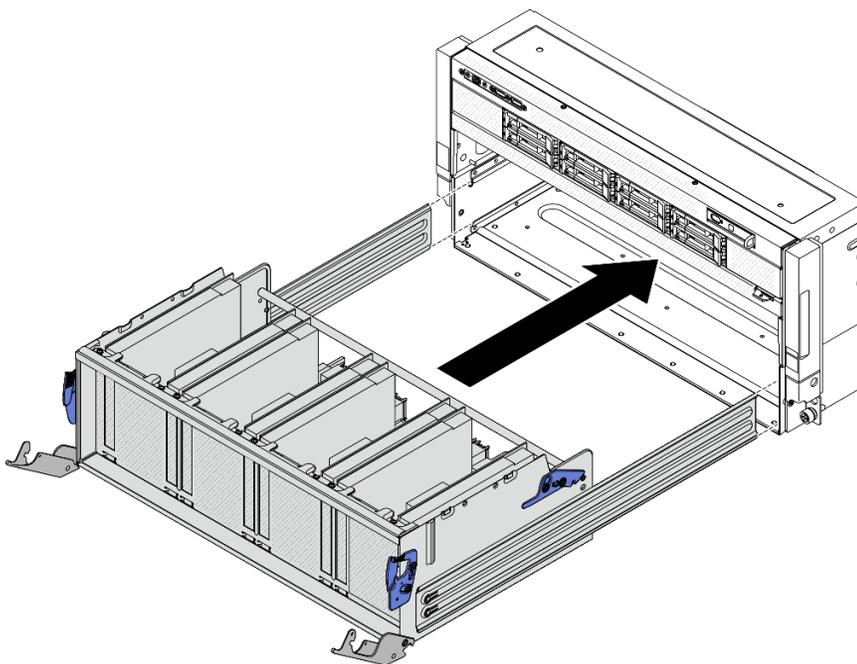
Instalação do alternador do comutador PCIe para a posição de parada
